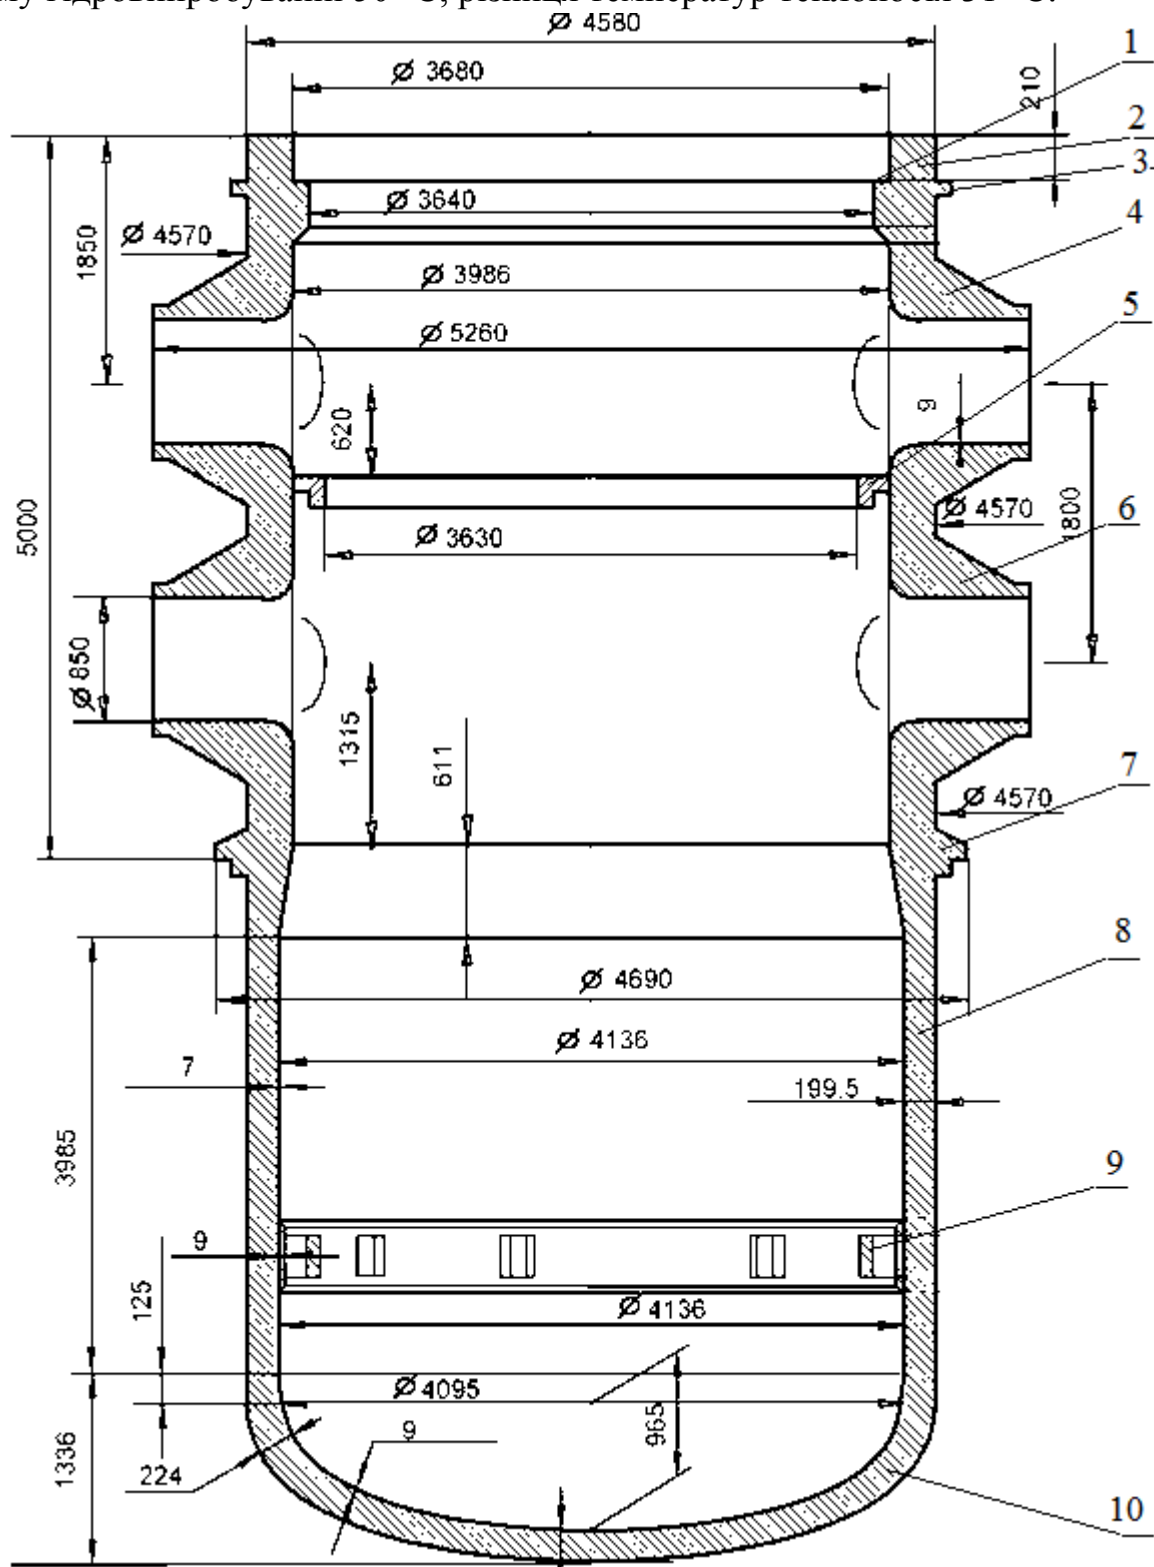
Корпус реактора ВВЕР-1000:
